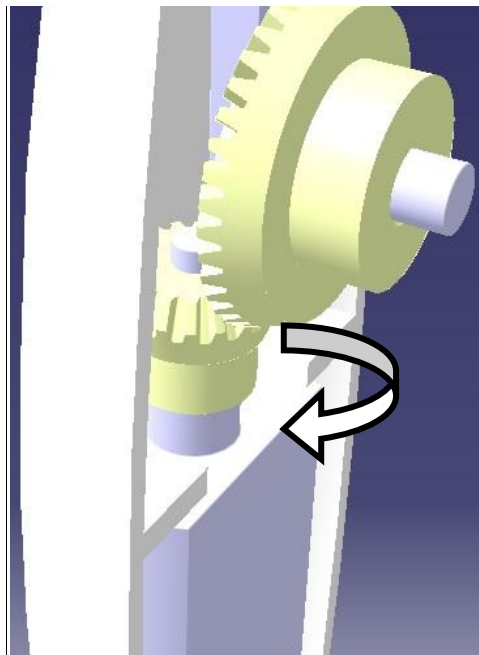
Transmisión del movimiento del Motor a Plastic Gear
